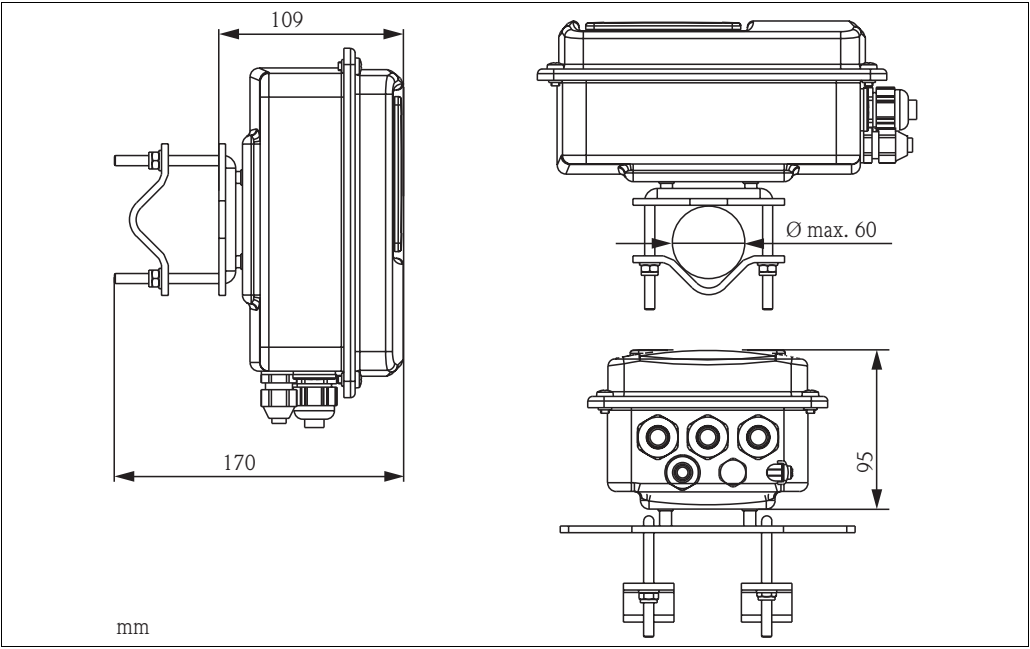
Montaje del CLD134 en tuberías Ø 60 mm
